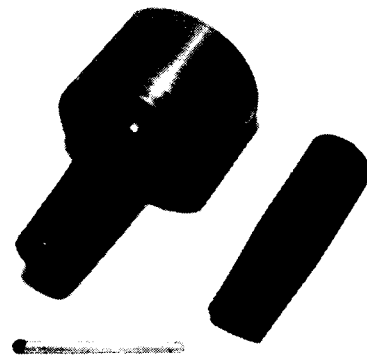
Электрод для точечной сварки диаметром 40 мм, изготовленный путем формирования рабочего участка наплавленным металлом из электрода диаметром 16 мм
